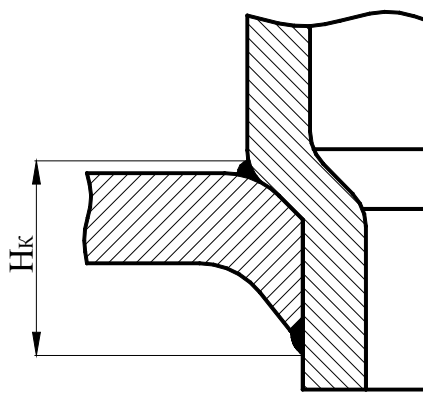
Сварное соединение с повышенной прочностью
